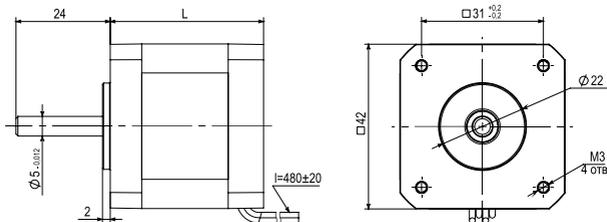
габаритные размеры шаговых двигателей серии SMO-17
